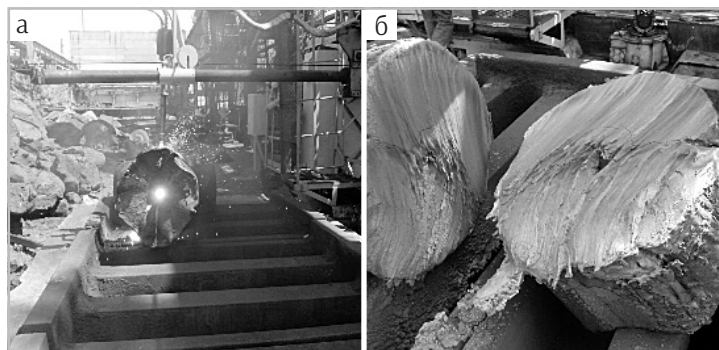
Резка конца поковки Ø 900 мм с закованной усадочной раковиной
